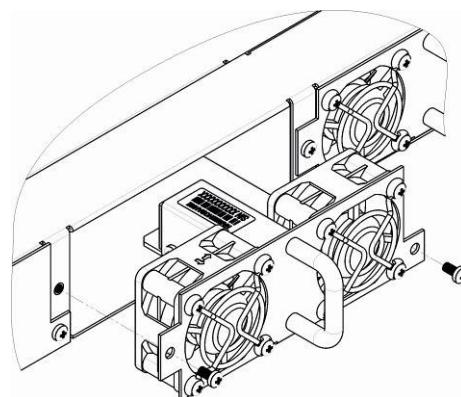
б – Блок вентиляции SMG-2016. Крепление в корпус
